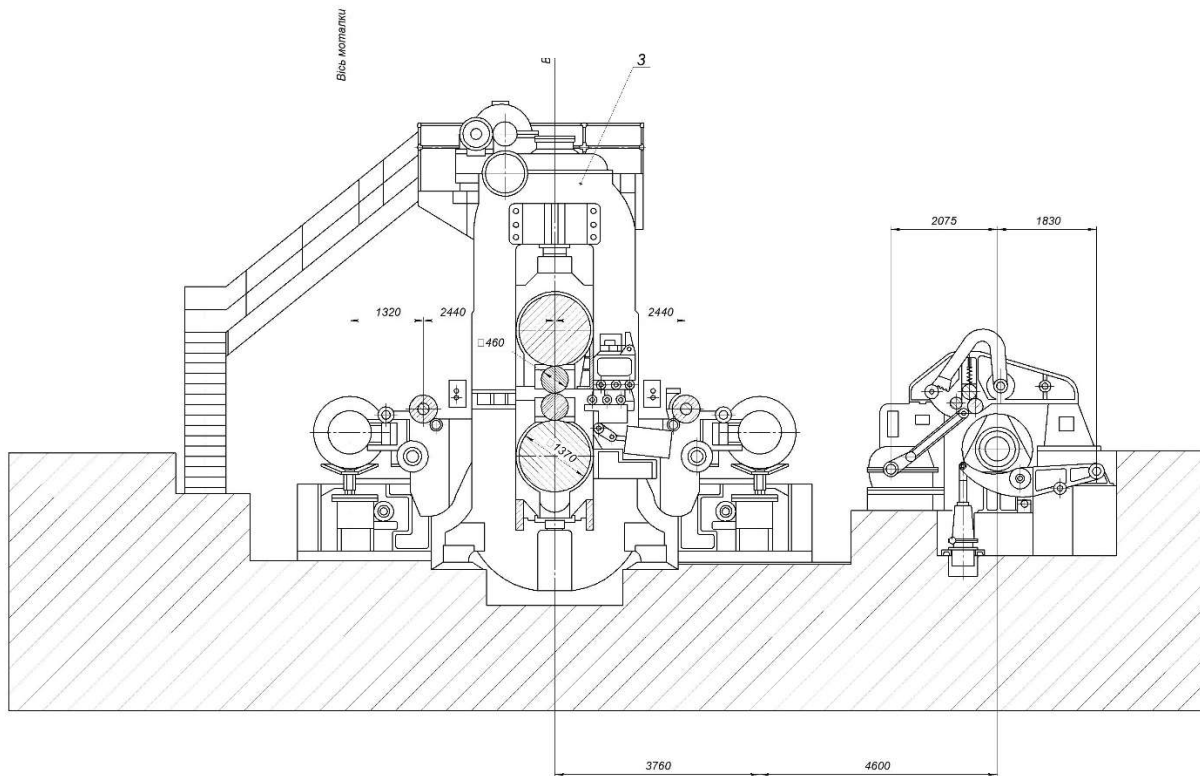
Реверсивний стан холодної прокатки 1680
